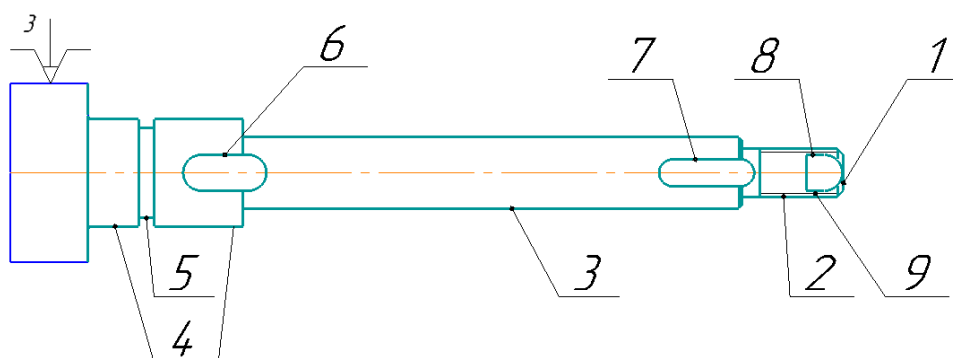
Эскиз обрабатываемой заготовки с пронумерованными поверхностями
